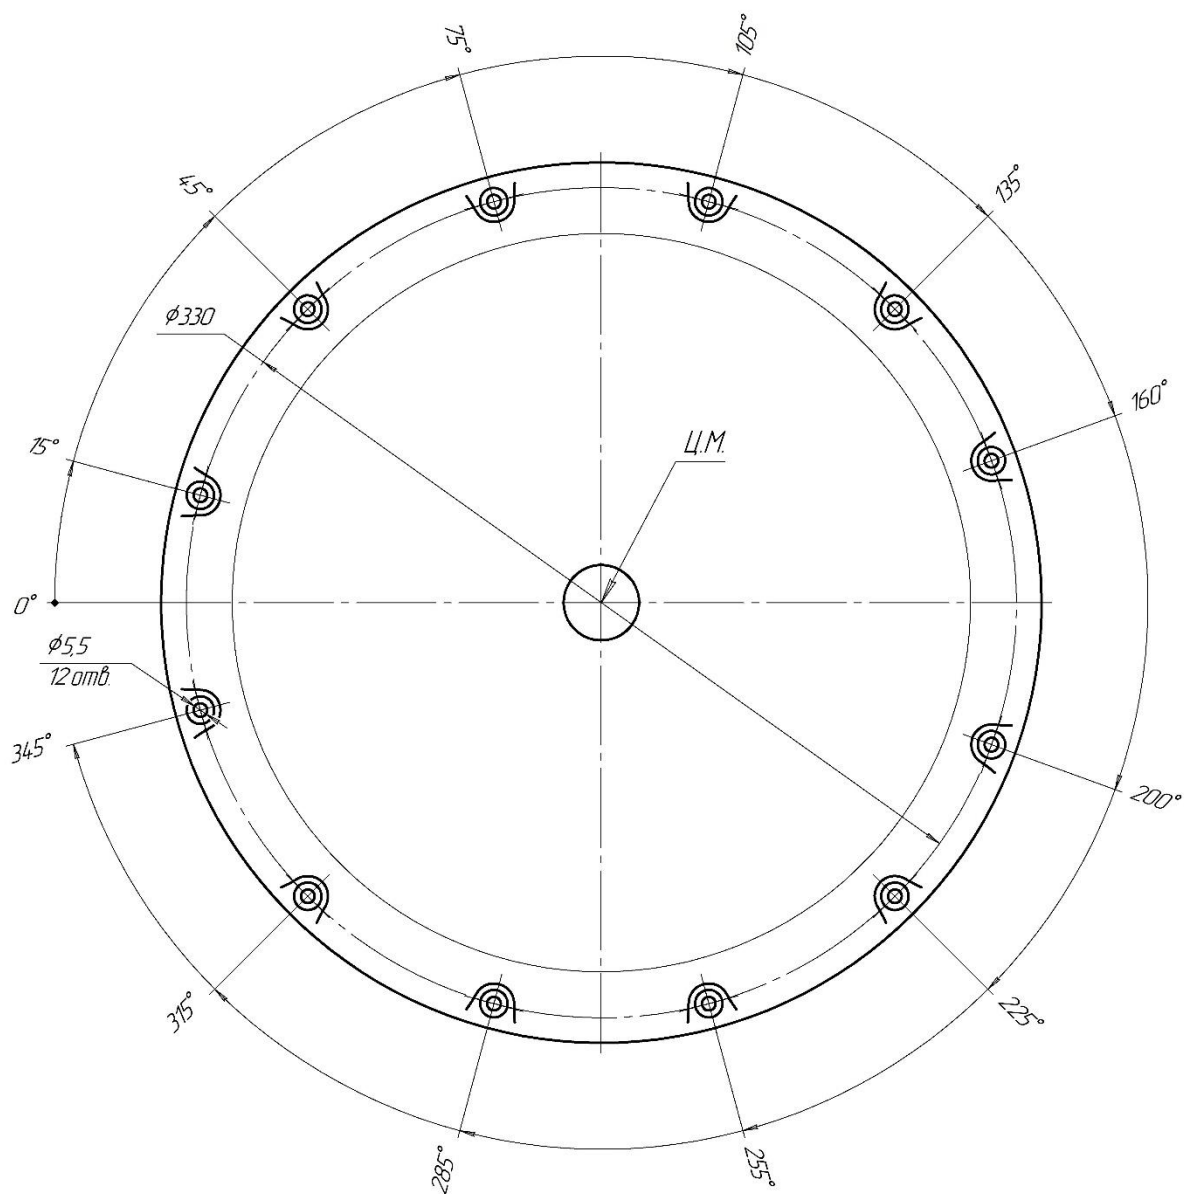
Габаритный чертеж блока Б15-РПА
